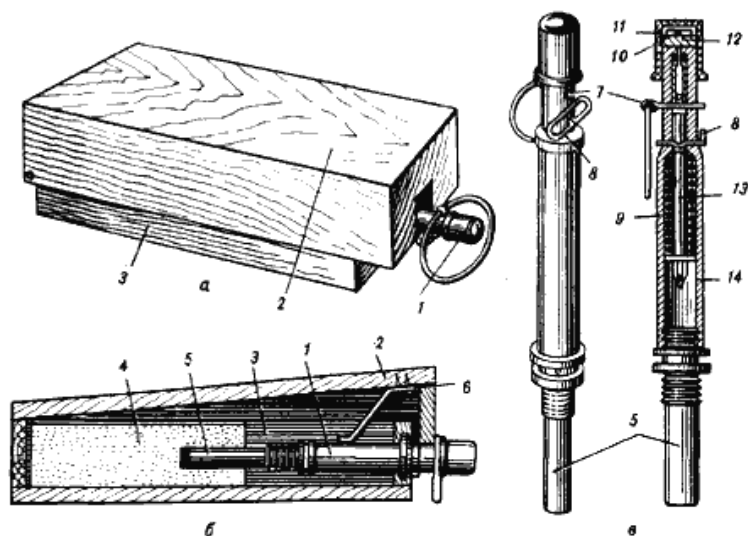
Противопехотная мина ПМД-6М: *а* — общий вид; *б* — разрез; *в* — взрыватель МУВ-2; 1 — взрыватель; 2 — крышка; 3 — корпус мины; 4 — заряд ВВ; 5 — запал; 6 — металлическая пластинка; 7 — предохранительная чека; 8 — Т-образная боевая чека; 9 — боевая пружина; 10 — резак; 11 — резиновый колпачок; 12 — металлоэлемент; 13 — ударник; 14 — корпус взрывателя
